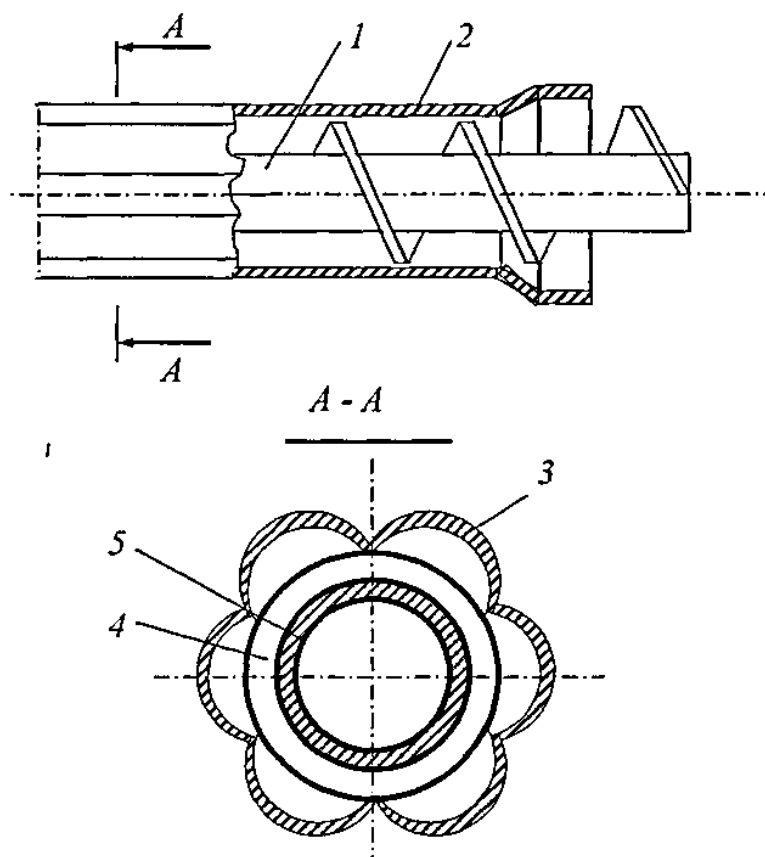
Схема шнекового конвейера с гофрированным кожухом.
